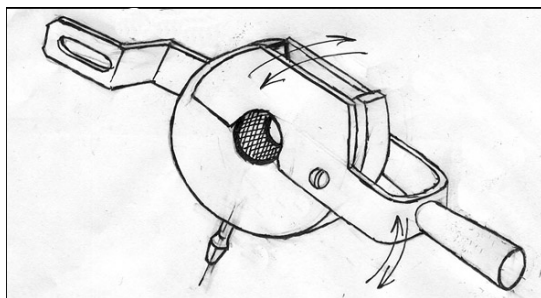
Съёмная камера для дополнительной защиты при ручной сварке стыков труб
